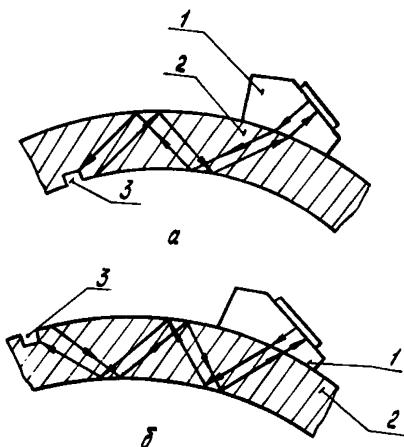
Контроль дефекта на внутренней поверхности 3-м отражением (а) и на наружной поверхности 4-м отражением (б): 1 - искатель; 2 - испытательный образец; 3 - искусственный дефект
